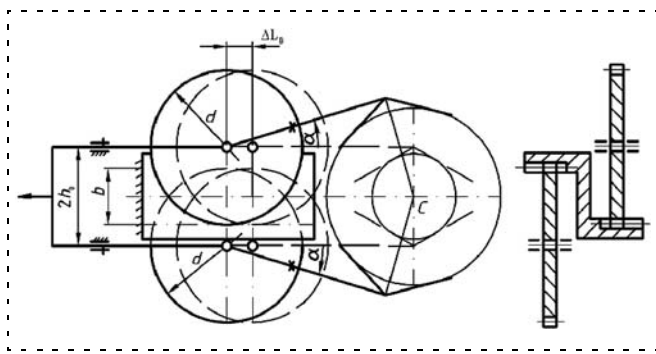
Преобразователь движения мехатронного модуля захватного устройства с подвижными колесами и Z-образной рейкой
